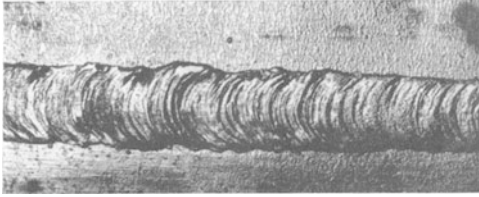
Aussehen einer Kupferschweißnaht an 5 mm-Blech.
